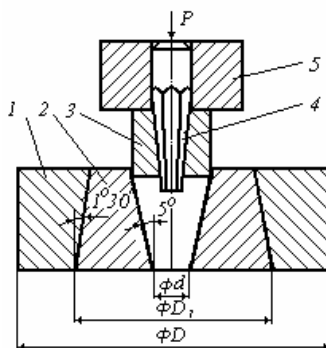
Приспособление для холодного выдавливания: 1 – матрица; 2 – обойма; 3 – заготовка; 4 – мастер-пуансон; 5 – стакан
